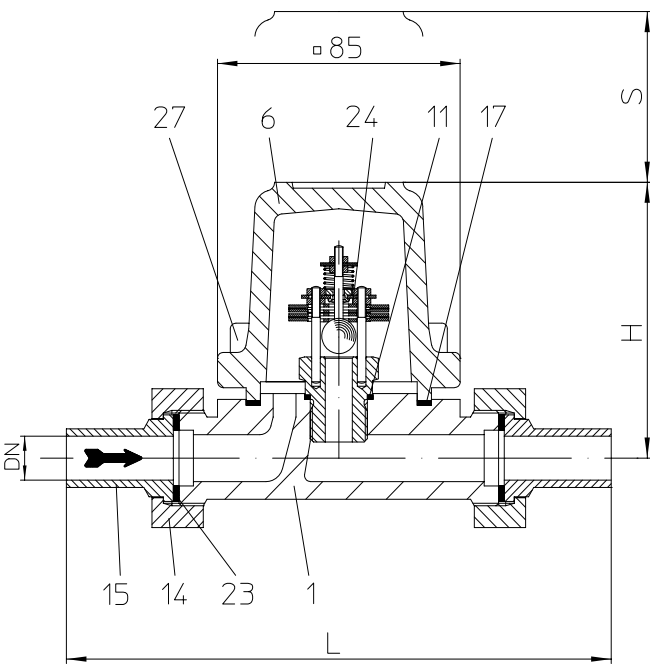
5 à raccord union à souder avec manchette à souder (seulement PN16)
